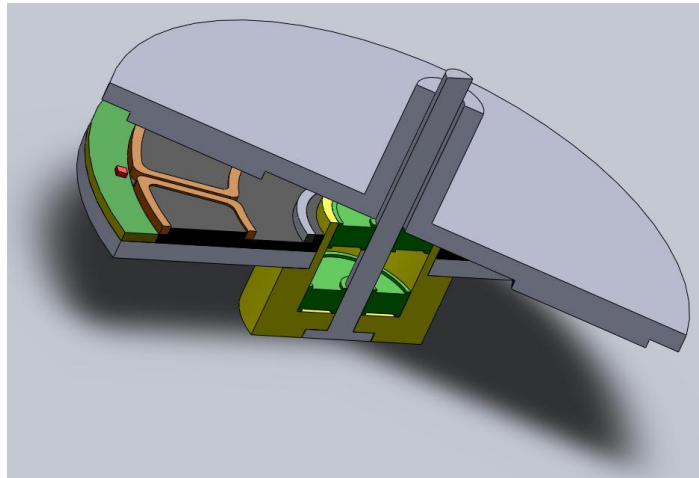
Vnitřní rotor motorku s radiálním tokem
